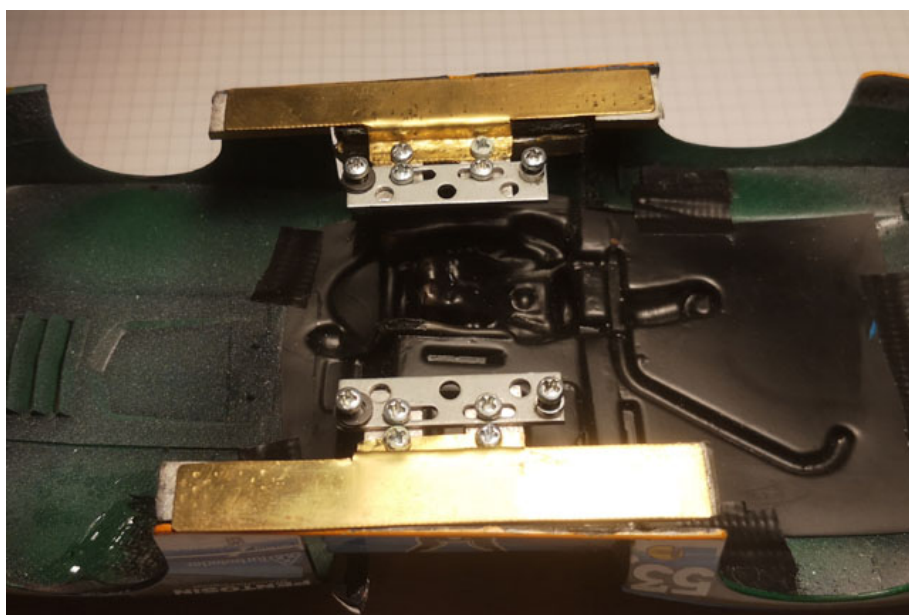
Beispiel Zusatzhalter aus Messingblech zur Aufnahme von Gewichten im Schwellerbereich der Karosserie eines Ford Capri Zakspeed.
